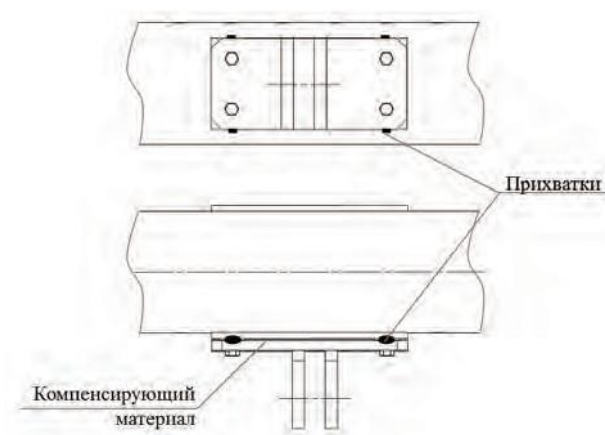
Схема фиксации кронштейна на раме сборочного приспособления
